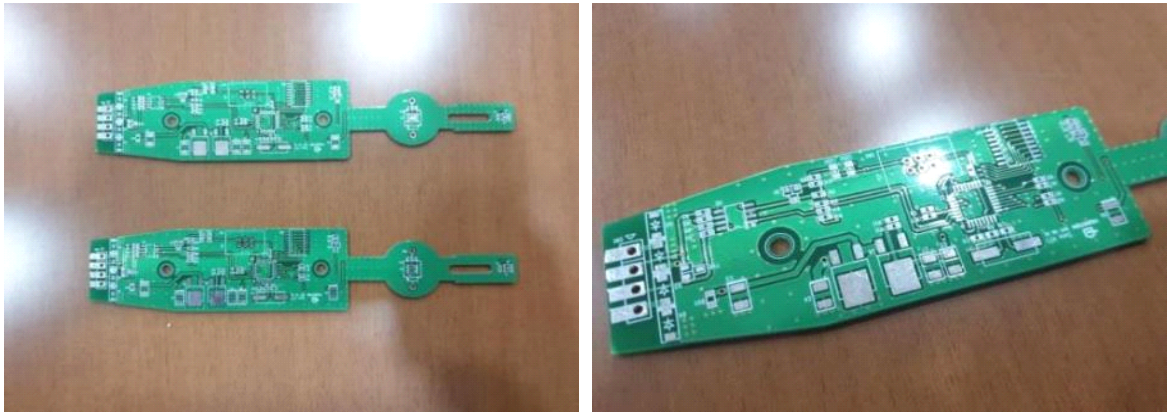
개별 온습도 센서 PCB 설계 및 제작 (1)
